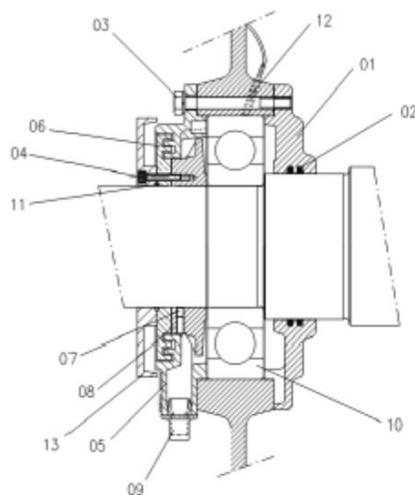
Строение смазываемого консистентной смазкой подшипника качения
